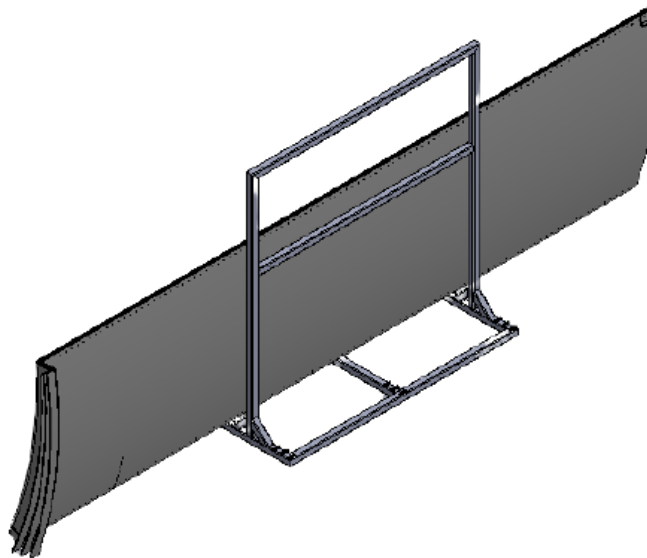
Cantilever con las placas del W-Tank. (Fuente: Indemat, departamento técnico)
